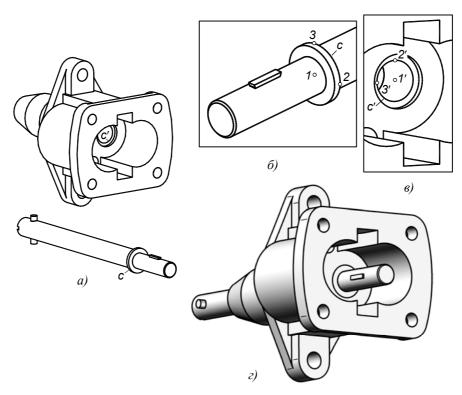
Установка вала в сборе в корпус насоса: a – загрузка вала в файл сборки; δ , ϵ – задание трех точек; ϵ – результат установки
